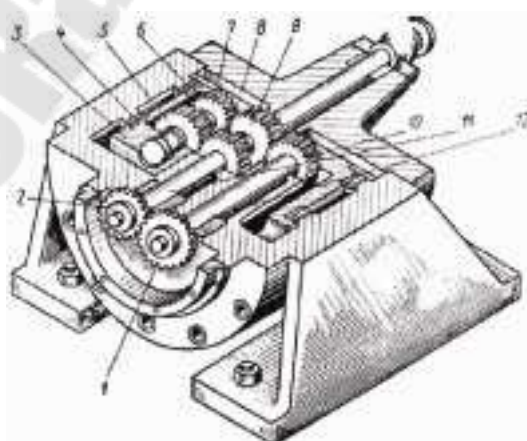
Стенд с перемещаемыми в окружном направлении отдельными зубчатыми колесами
